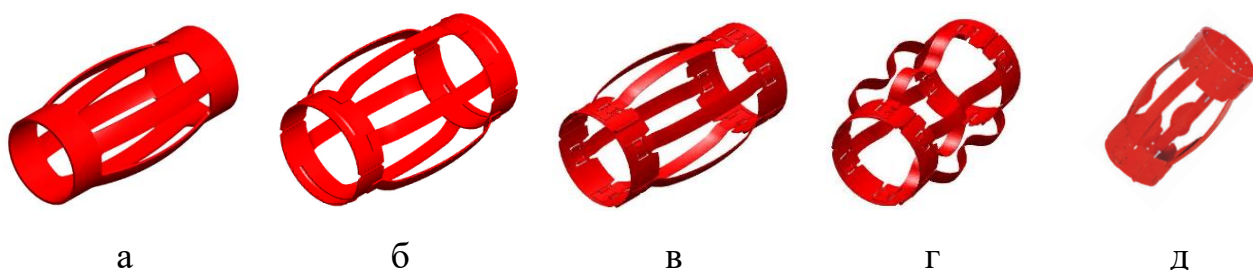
Упругие центраторы: а – неразъёмный пружинный центратор; б – сварной пружинный центратор; в – составной пружинный центратор; г – полужесткий пружинный центратор; д – пружинный центратор-турбулизатор.
